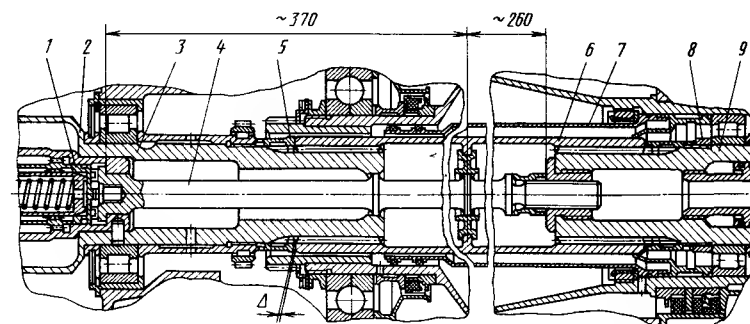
Соединение валов турбины и компрессора с помощью трубчатой рессоры и стягивающего болта (штанги) ТРДД АИ-25
